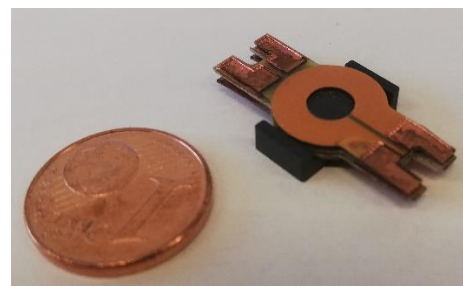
Assemblage de quatre couches non brasées sur un demi pot.
